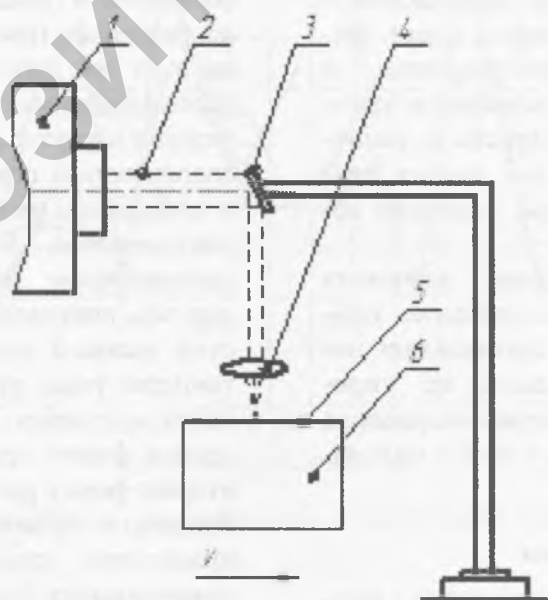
Схема лазерной установки: 1 – разрядная трубка; 2 – лазерный луч; 3 – поворотная оптика; 4 – фокусирующая оптика; 5 – упрочненная поверхность; 6 – деталь
